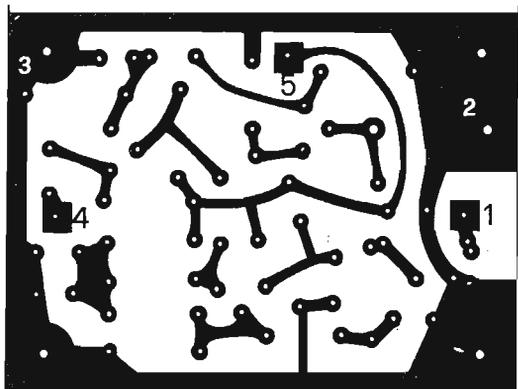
Disegno del circuito stampato sul quale si realizza il cablaggio del convertitore. Si tenga presente che questo disegno è in scala unitaria.
